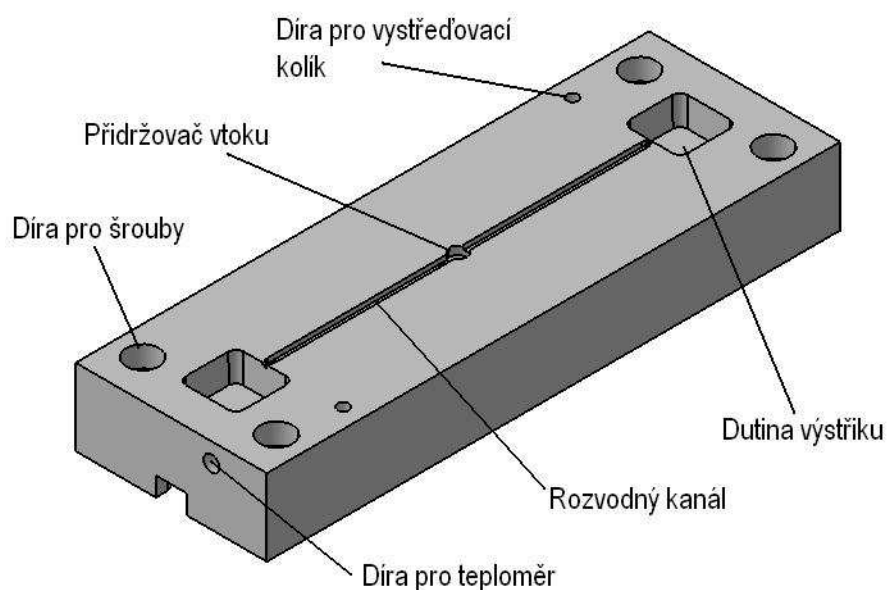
Spodní strana formy (deska s přímým úzkým kanálem)
